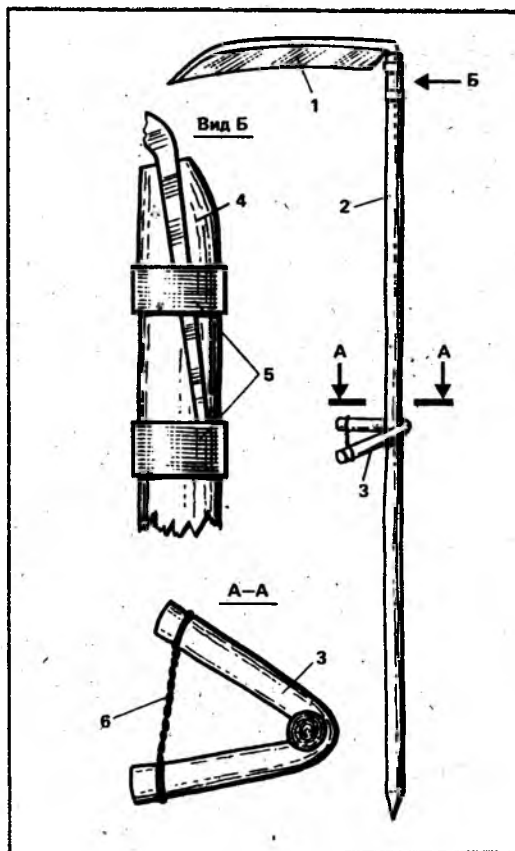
Коса: 1 — нож косы; 2 — косовище; 3 — ручка; 4 — клин; 5 — кольца; 6 — шпагат
